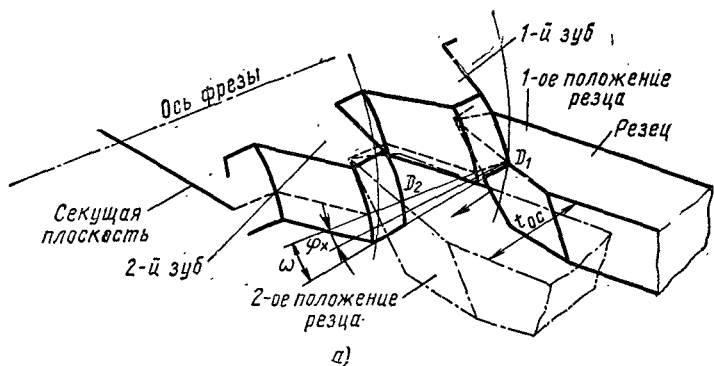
Схема затылования боковых сторон профиля червячной фрезы
